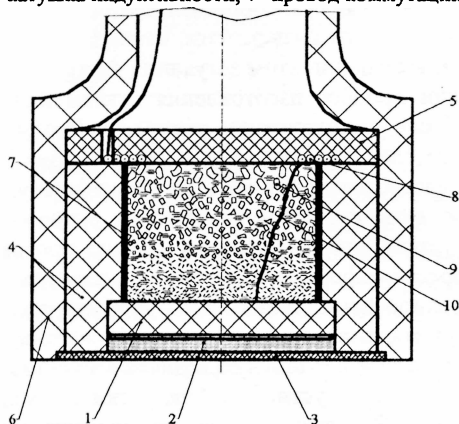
Вид А (зонда новой конструкции): 1- пьезокерамическая пластина; 2- первый согласующий слой; 3- второй согласующий слой; 4- втулка акустической развязки; 5- катушка индуктивности плоской формы; 6- металлический корпус; 7- слой магнетострикционного металла; 8- витки катушки индуктивности; 9- гранулы пьезокерамического порошка; 10- провод коммутации.
